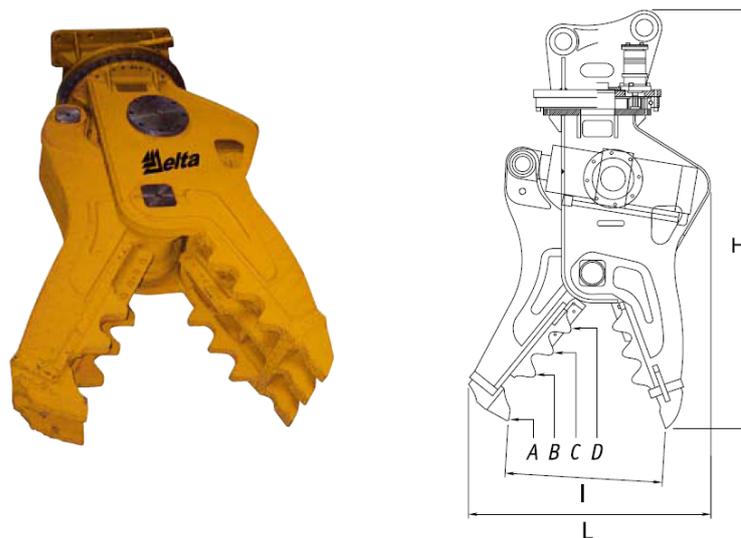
Конструктивная схема полноповоротных гидророжниц для измельчения бетонных конструкций
